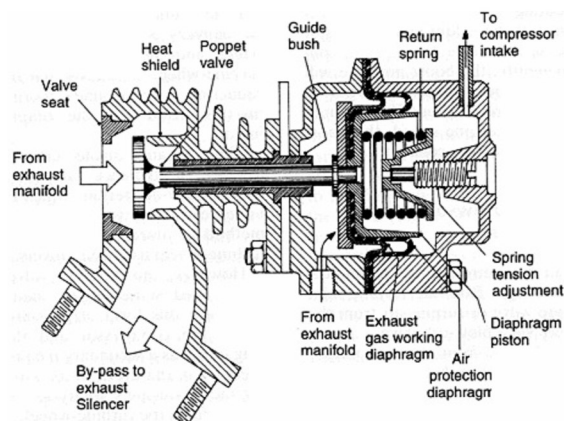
Componentes que constituem uma *wastegate*, incluindo o atuador pneumático (Heisler, 1995).
